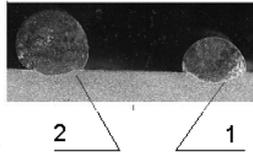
Форма валиков, наплавленных трехфазной дугой:
